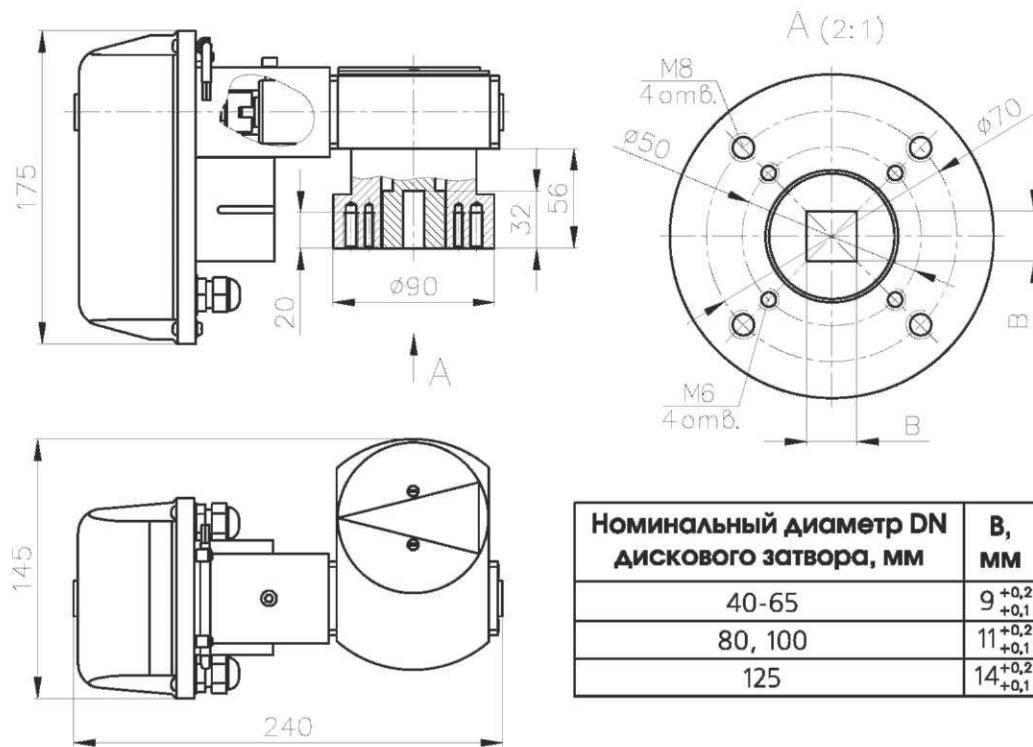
Габаритные и присоединительные размеры ЭИМ
